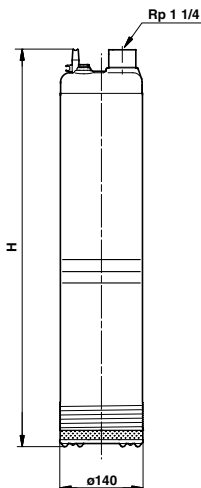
SBA-Pumpe. Gleiche Abmessungen mit eingebautem und mit schwimmendem Zulaufsieb.
